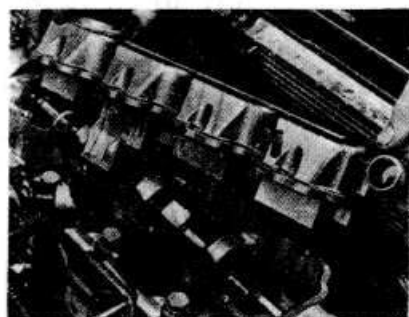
Снятие крышки распредвала с головки блока цилиндров
